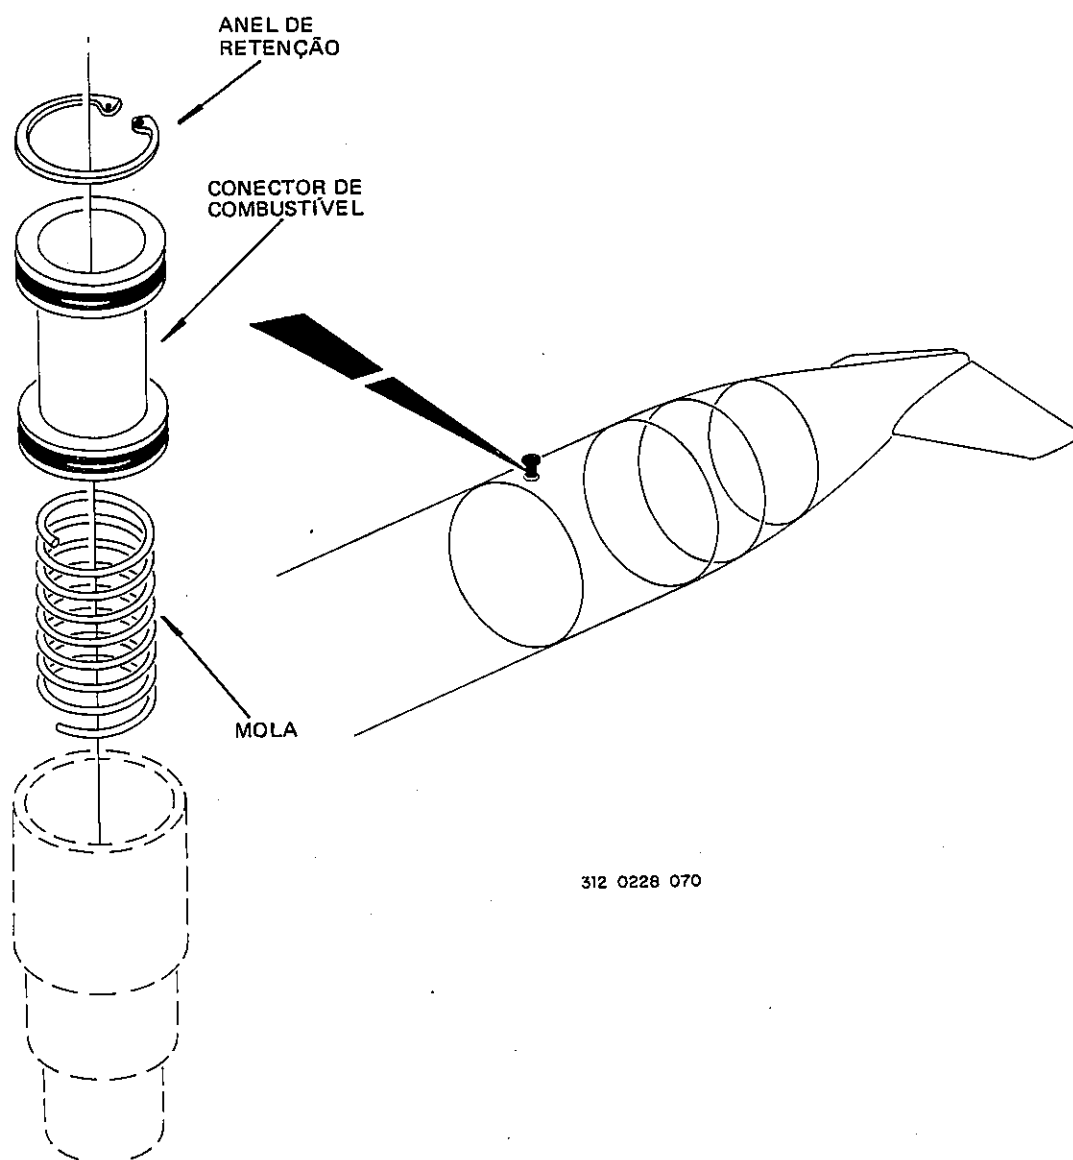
Remoção da Mola do Conector de Transferência de Combustível
